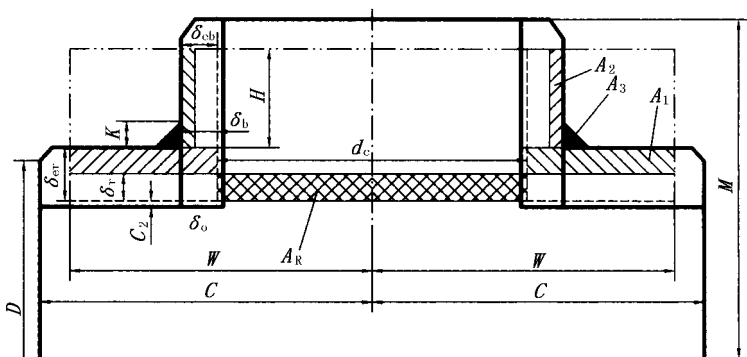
整体焊接三通补强计算示意图
